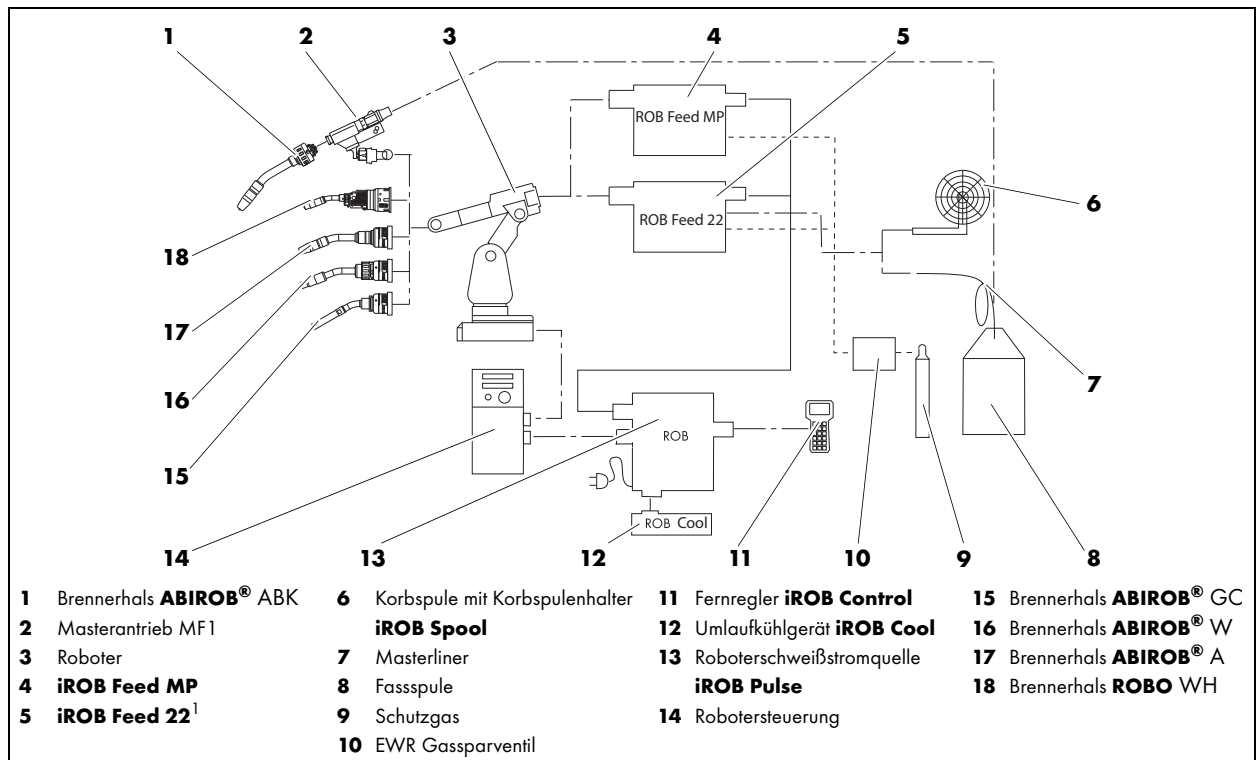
Komponenten Roboterschweißsausrüstung
